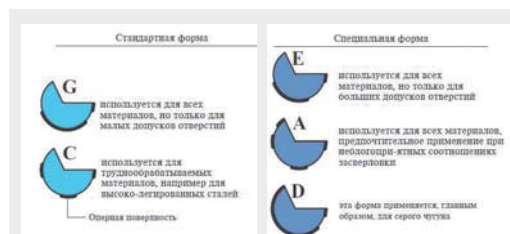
Сверла с опорными поверхностями типа A, C, E, D, G
